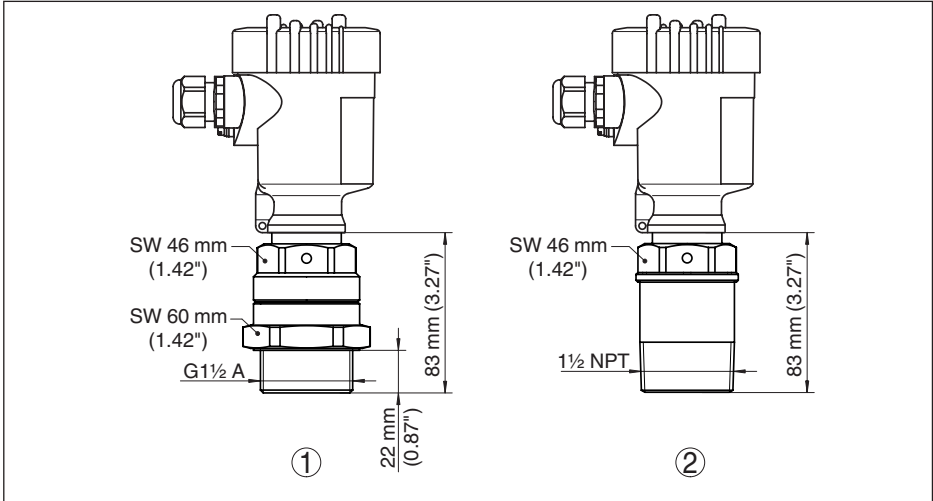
VEGAMIP 61, innenliegende Hornantenne (Gewindeausführung)
